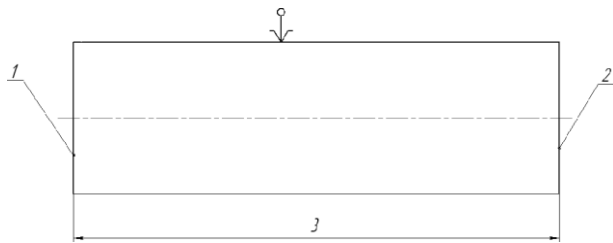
Креслення заготовки з необхідними розмірами 020 Токарна з ЧПУ
